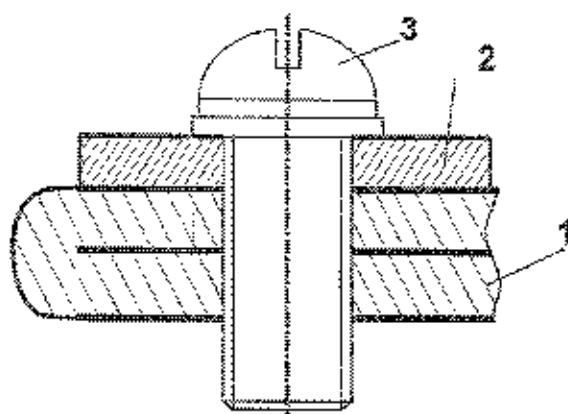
Увеличение длины свинчивания за счет гибки листа: 1 – заготовка; 2 – накладка; 3 – винт [3]
